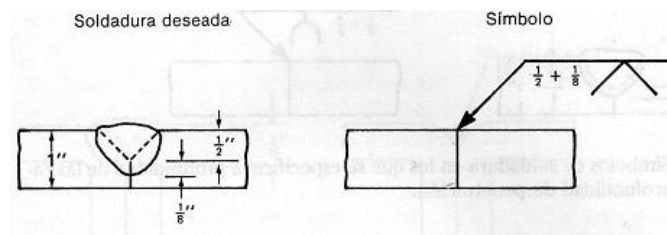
Símbolo de soldadura con especificación de la penetración en la raíz.
